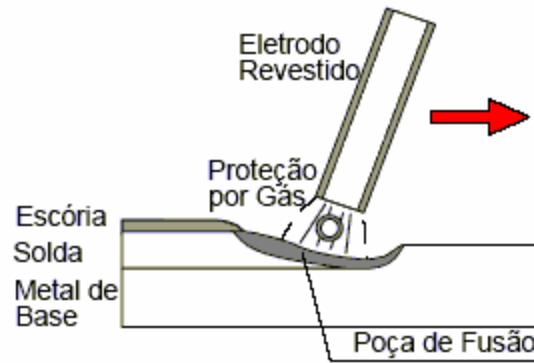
Solda por Eletrodo Revestido (MODENESI e MARQUES, 2000)
